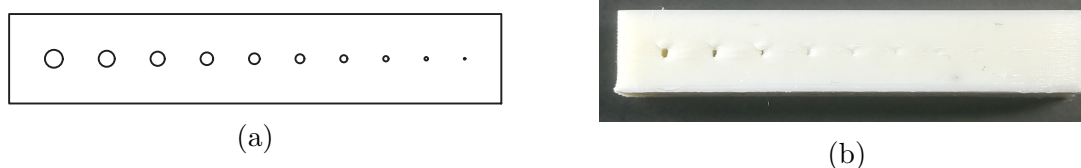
En (a) esquema de la pieza a imprimir para determinar el mínimo tamaño de agujero. En (b) foto de la geometría fabricada por la impresora Ultimaker.
